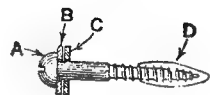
Montaje de tornillo de madera y arandelas; A, tornillo de madera, $4,75 \times 57$ milímetros; B, arandela de acero, 12,7 mm de diámetro exterior, 5,5 mm diámetro del agujero, 1,5 mm de grosor; C, arandela de fibra; D, la punta del tornillo está recubierta de cera de abejas en 25,4 mm.
